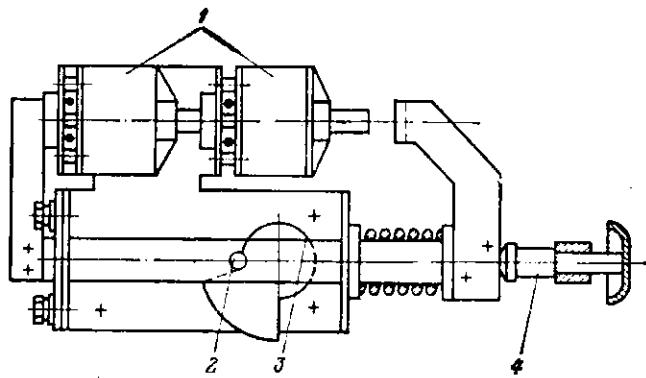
Конструкция блокировки валика рукоятки разъединителя с кнопкой «Стоп»
